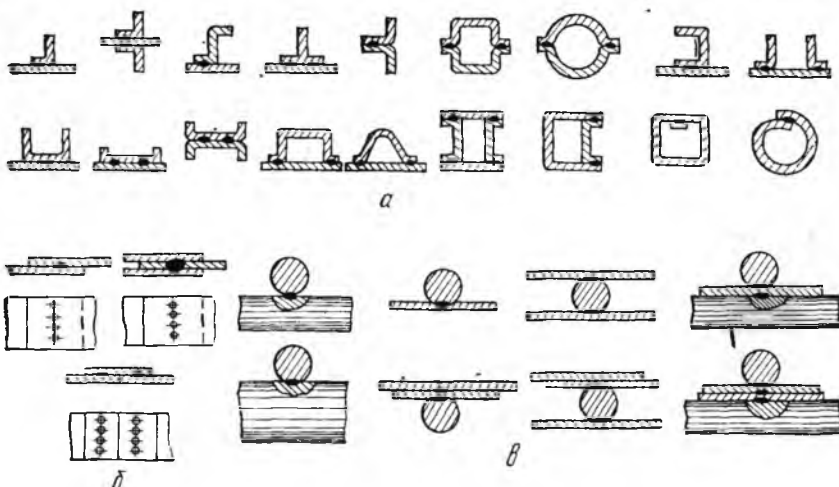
Типы соединений и сварные узлы, выполняемые точечной конденсаторной сваркой:
